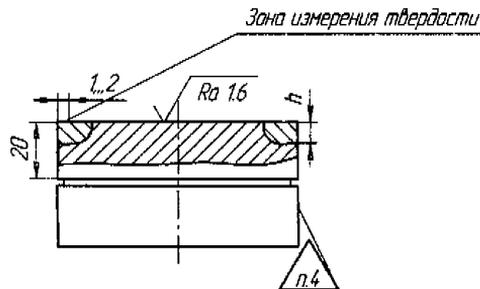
Образец для замера твердости деталей с плоским уплотнением
